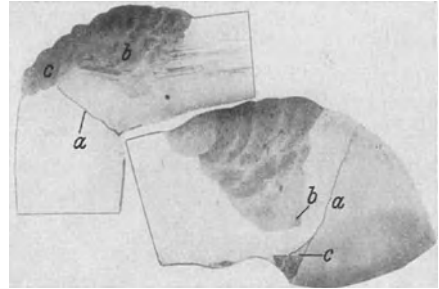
Elektrische Fehlschweißungen bei der Ausbesserung einer Wasserkammer ($V = 1$).
